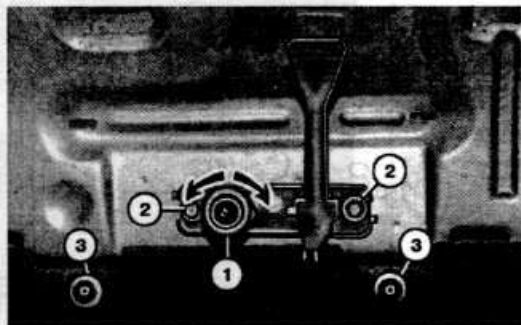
Расположение мест регулировки и крепления деталей капота:
